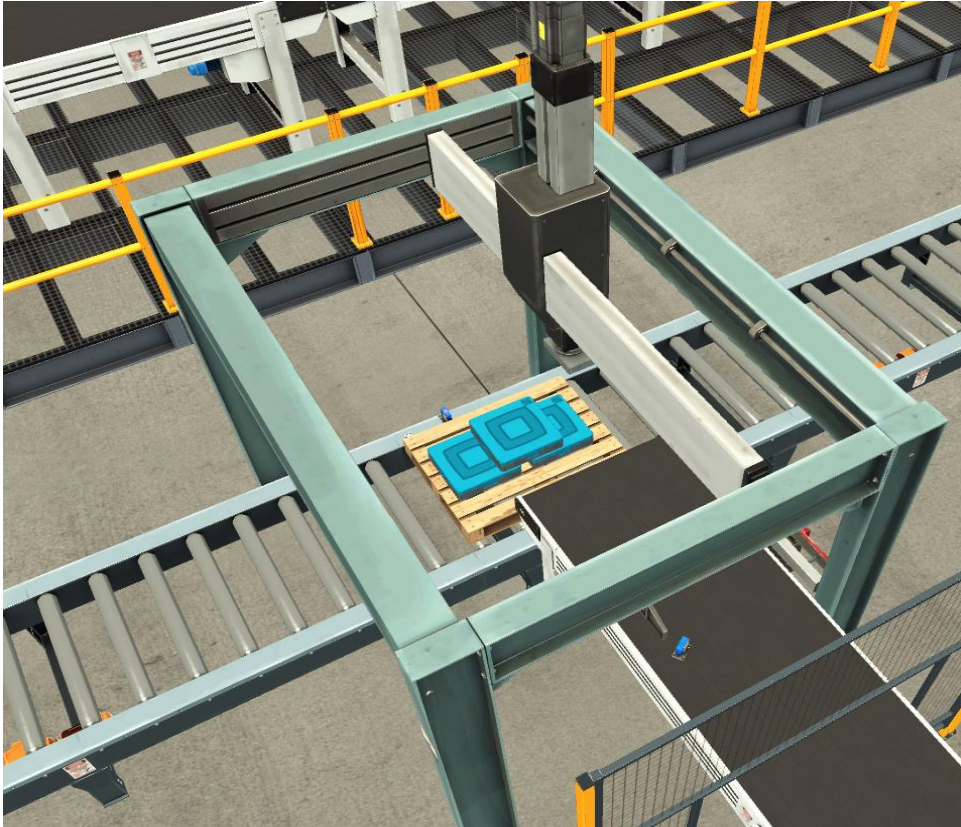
Ejemplo de Pick and Place de tres ejes con el pallet de cajas azules formad.
